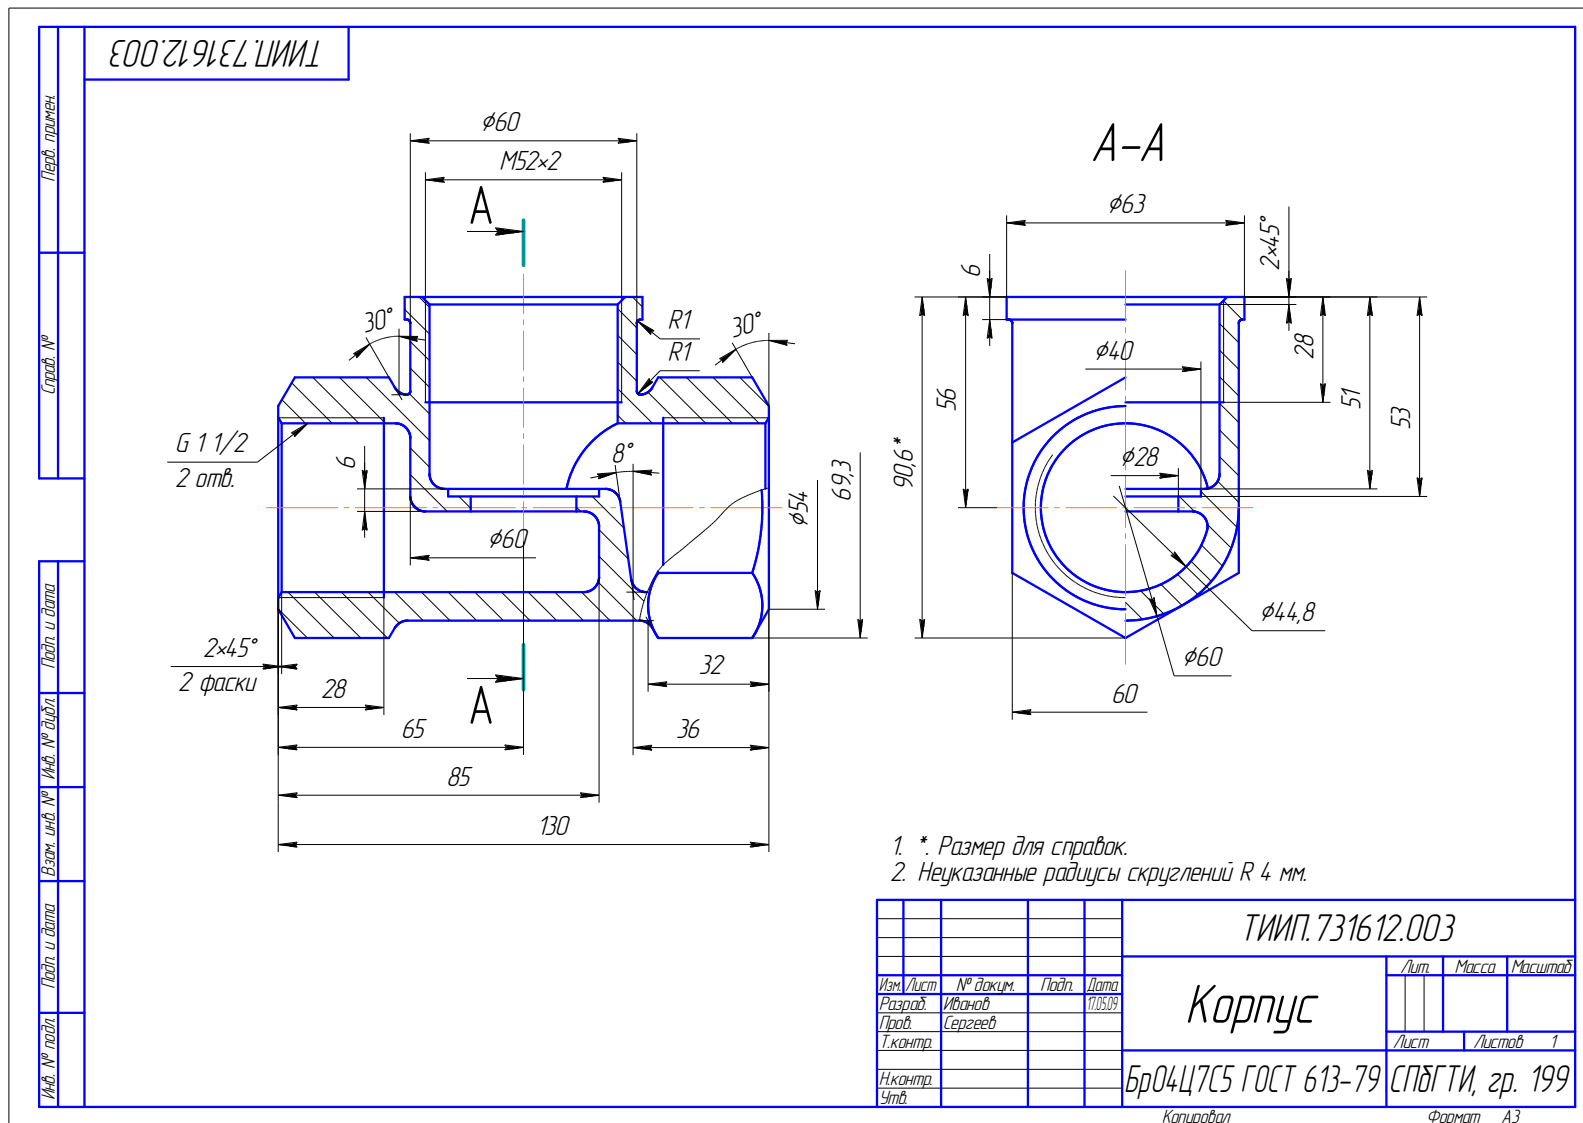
Пример оформления эскиза (рабочего чертежа) корпуса
